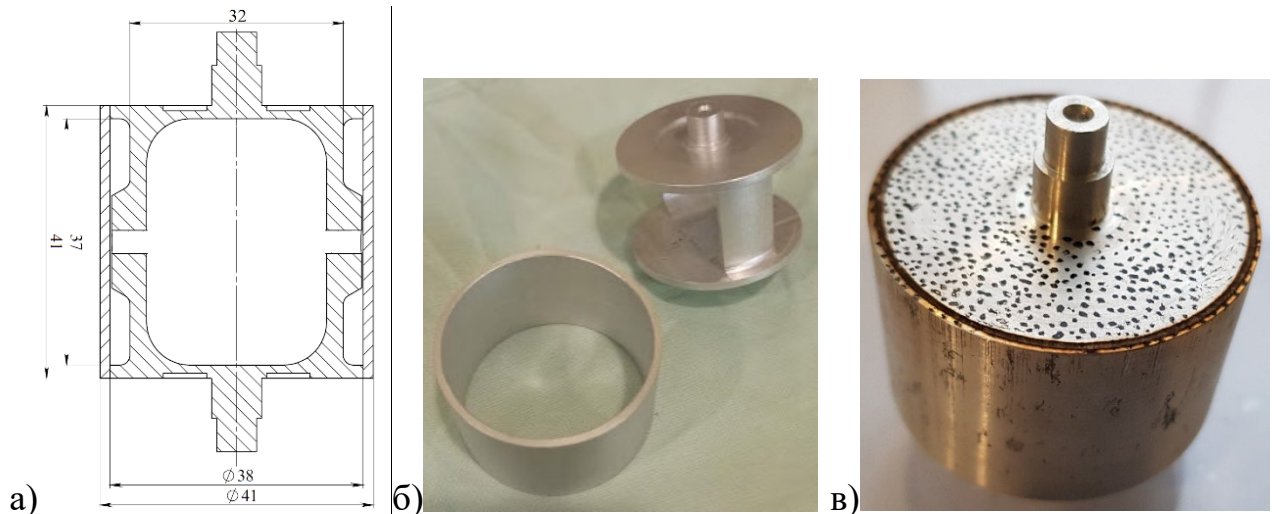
Виріб, що зварюється: а) переріз; б) деталі, що з'єднуються зварюванням; в) загальний вигляд після зварювання
